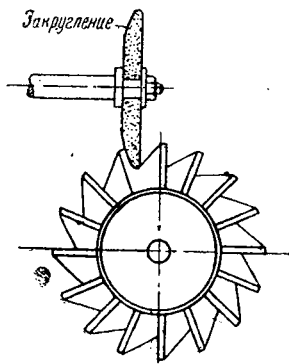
Заточка подзубка фрезы со спиральными зубцами.
